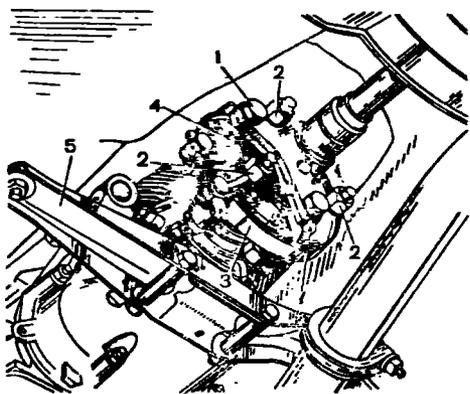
Эластичная муфта соединения карданного вала с коробкой передач: 1 - болты крепления фланца карданного вала к эластичной муфте; 2 - гайки болтов крепления фланца вторичного вала коробки передач к эластичной муфте; 3 - приспособление А.70025; 4 - эластичная муфта; 5 - поперечина задней подвески двигателя
